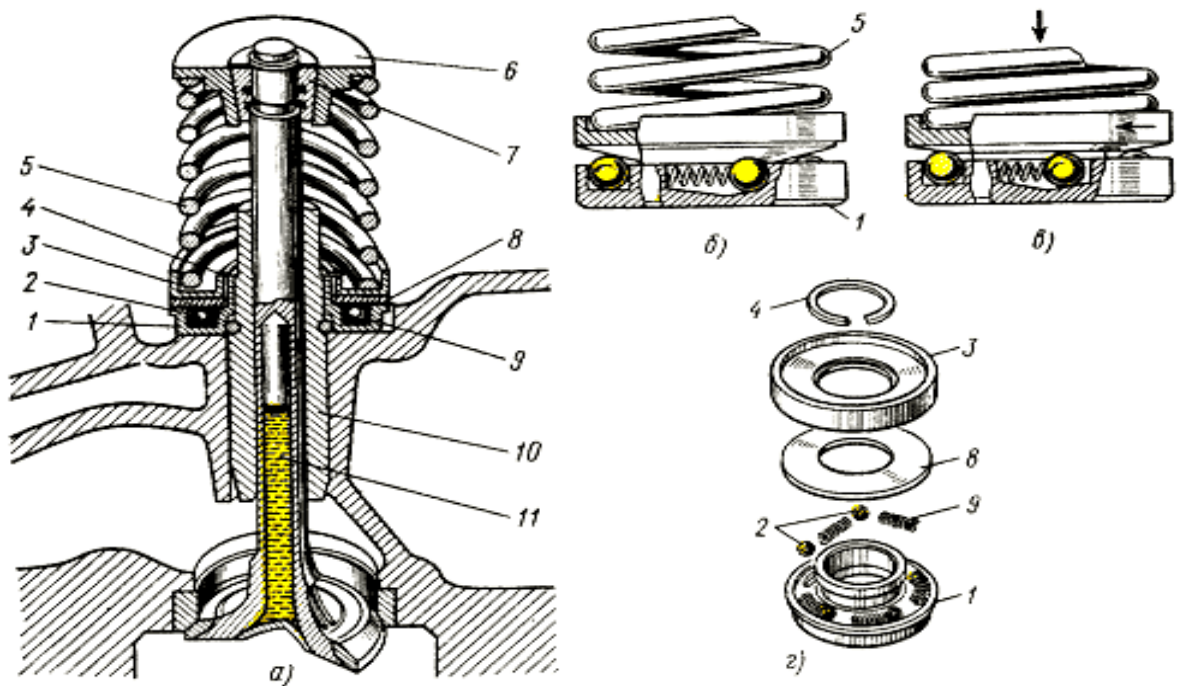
Випускний клапан: а - випускний клапан, б - клапан закритий, в - клапан відкритий, г - деталі механізму 1 - корпус механізму повороту; 2 - кульки; 3 - опорна шайба; 4 - замкове кільце; 5 - пружина клапана; 6 - напoлeгливa шайбa пружини; 7 - сухарики; 8 - дискова пружина; 9 - поворотна пружина; 10 - напрямна втулка; 11 - металевий натрій
